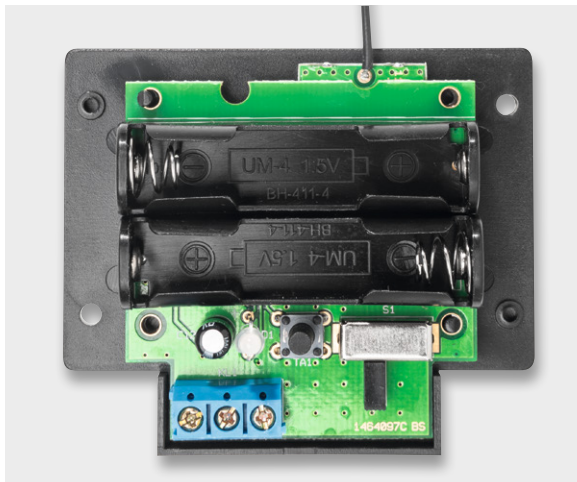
Die auf die Gehäuseunterseite aufgelegte Platine
